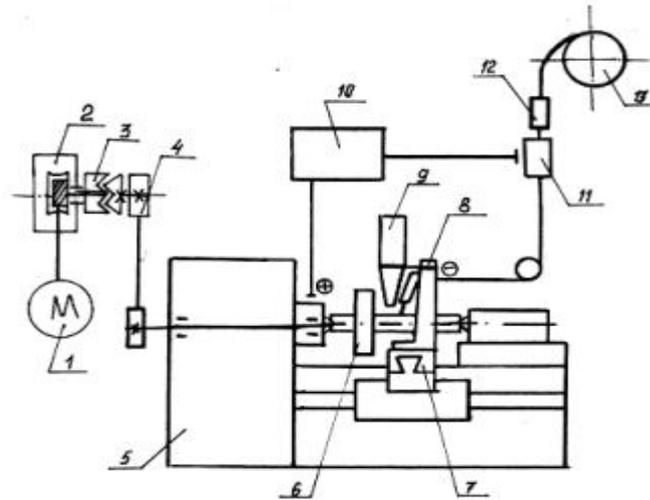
Схема установки для механизированной наплавки под флюсом:
